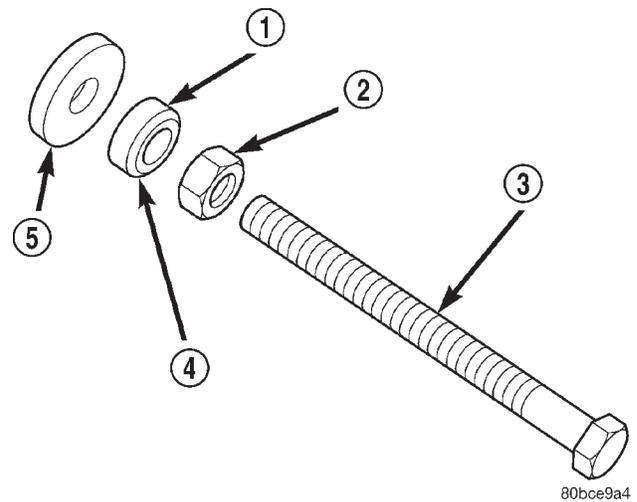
Richtige Montagemethode für Spezialwerkzeug 8512
